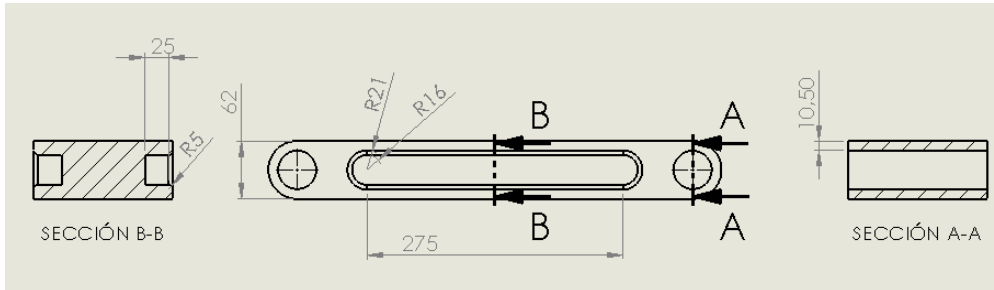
Plano barra BD reforzada y con rebaje en SolidWorks.
